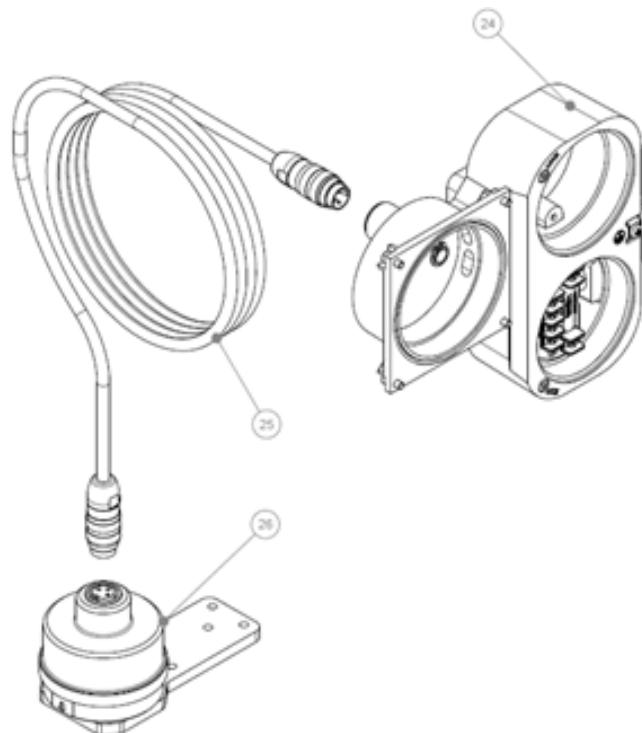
Desenho explodido do sensor remoto do VVP10.
